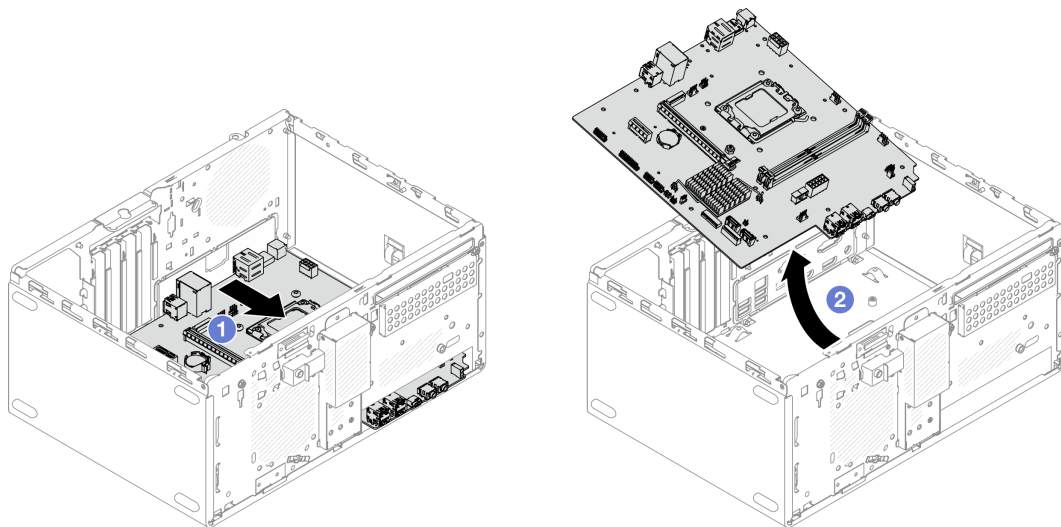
Entfernen der Systemplatine aus dem Gehäuse
